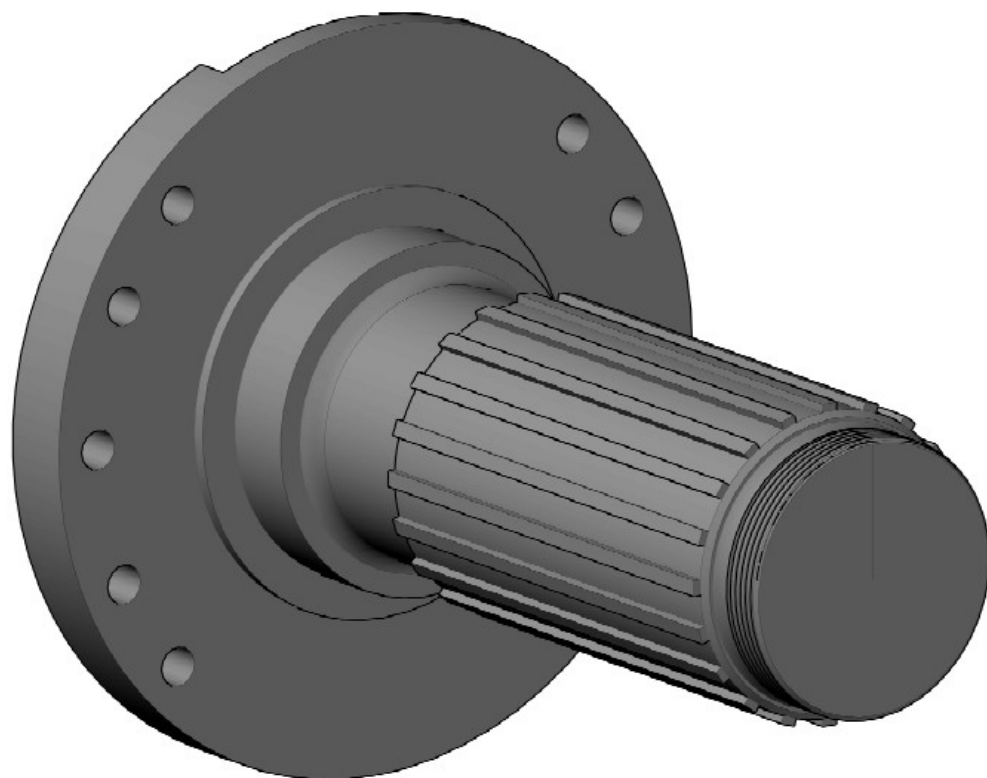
3D креслення деталі шліцевого валу
